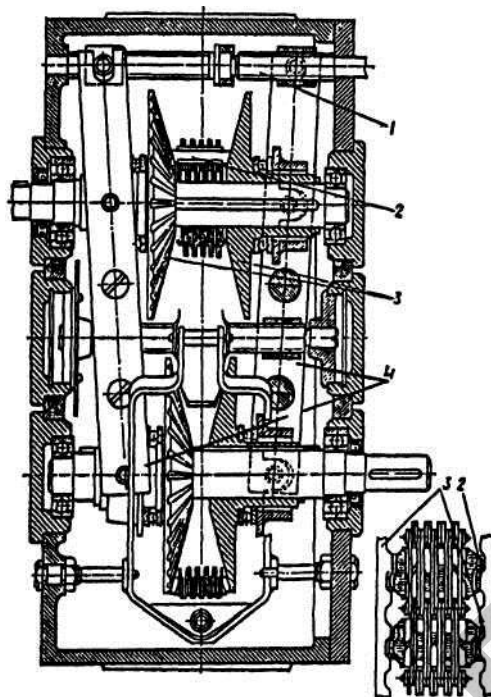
Цепной вариатор: 1 — винт; 2 — цепь; 3 — диски; 4 — рычаги
